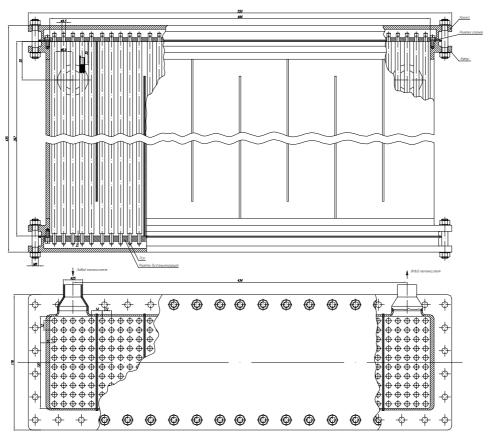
Конструкция корпуса реактора РУ МАРС с установленными твэлами
